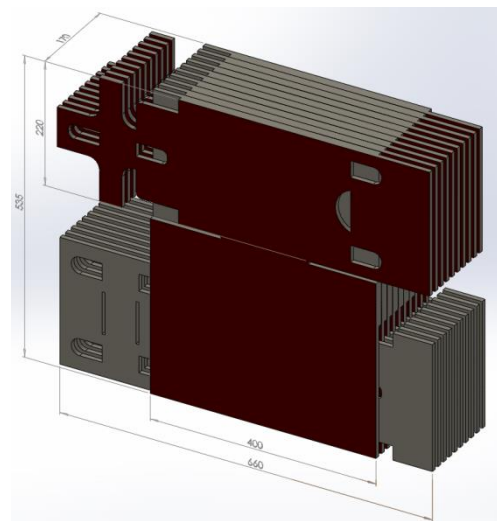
Croquis Real y Paletizado Planta Troquelada irregular.
